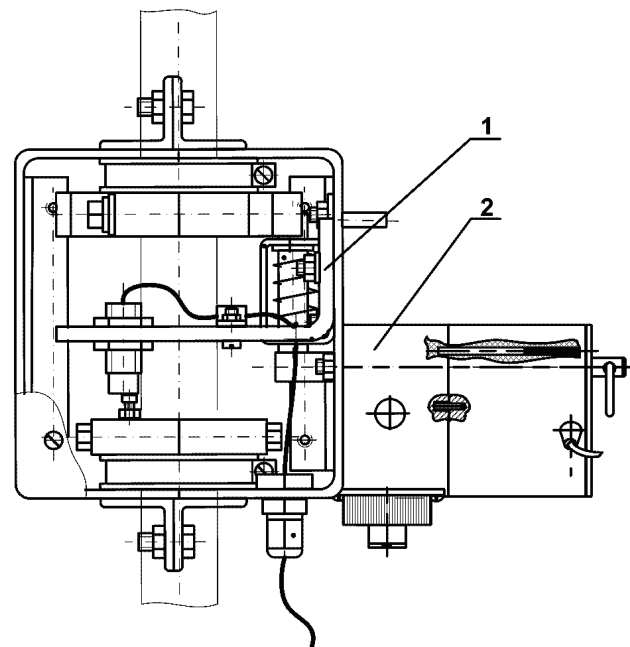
Устройство блокировки УБ – 1: 1 – оборудование ОББ, 2 – опытный образец № 5
